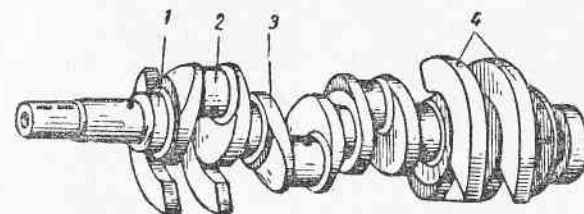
Коленчатый вал двигателя ЯАЗ-204:
